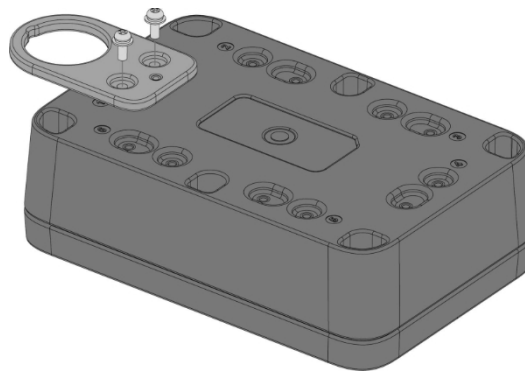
Befestigung der Haken-Schlaufen-Halterung am Gehäuse
